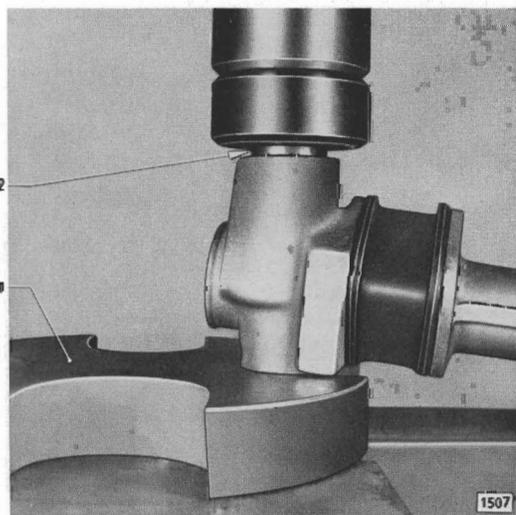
Dichtringfassung in Lenkgehäuse eindrücken
